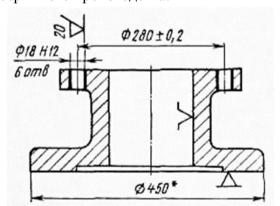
Фрагмент рабочего чертежа детали
